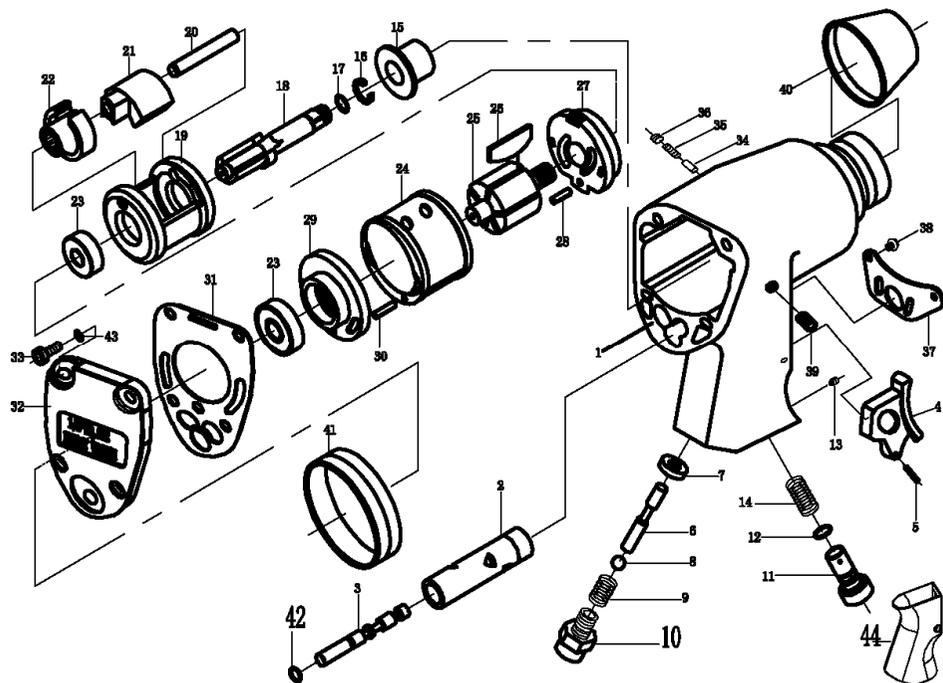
Схема устройства и сборки гайковерта ручного пневматического MFW 012/244-1
